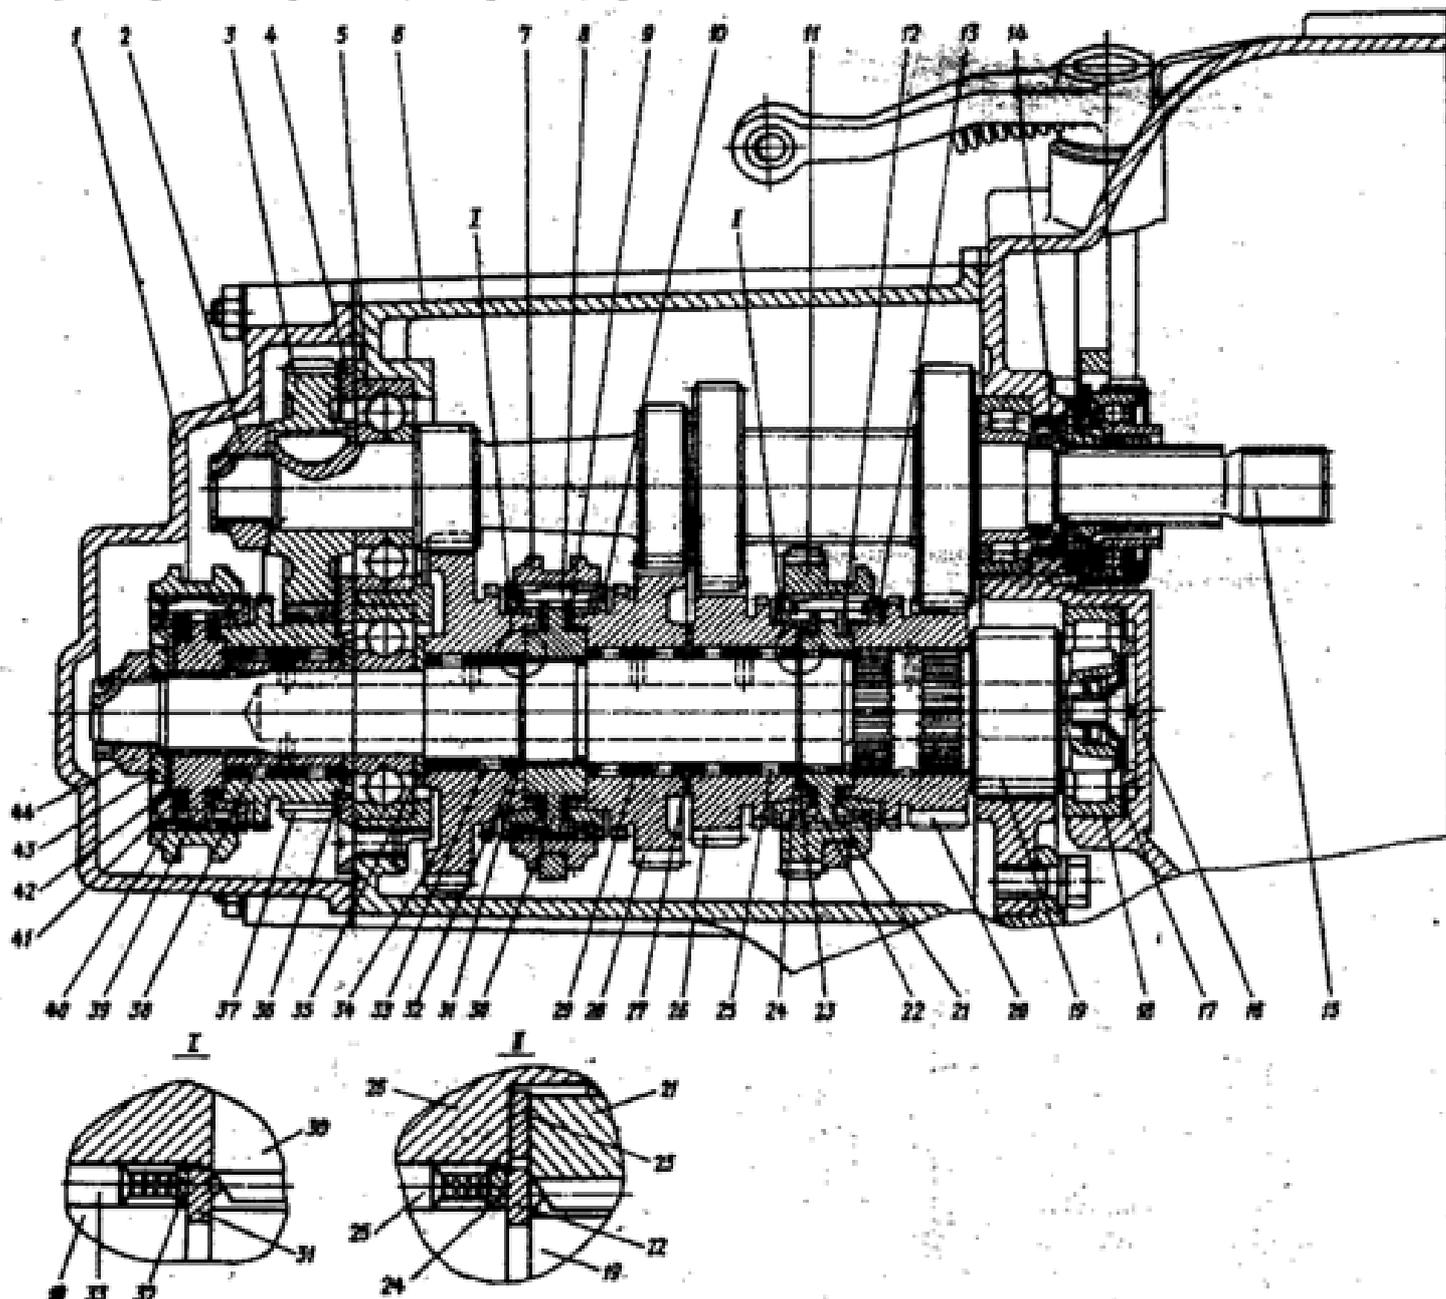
Коробка передач, продольный разрез: 1 - задняя крышка; 2, 44 - гайки; 3 - ведущая шестерня пятой передачи; 4 - крышка подшипников; 5, 18 - подшипники; 6 - картер коробки передач; 7 - муфта включения первой и второй передач; 8 - сухарь синхронизатора; 9, 12 - пружины синхронизаторов первой-второй и третьей-четвертой передач; 10, 13 - кольца блокирующие синхронизаторов первой-второй и третьей-четвертой передач; 11 - шестерня ведомая заднего хода; 14 - манжета; 15 - ведущий вал; 16 - картер сцепления; 17 - маслоотражательная шайба; 19 - шестерня-вал ведущая главной передачи; 20, 26, 28, 34, 37 - ведомые шестерни четвертой, третьей, второй, первой и пятой передач; 21 - ступица ведомой шестерни заднего хода; 22, 31 - стопорные кольца; 23, 27 - упорные шайбы; 24, 32 - кольца; 25, 33 - игольчатые подшипники; 27 - проставочные кольца; 30 - ступица муфты включения первой и второй передач; 35, 36 - упорные шайбы; 38 - распорная втулка; 39 - ступица муфты пятой передачи; 40 - муфта включения пятой передачи; 41, 42 - упорные шайбы сухарей пятой передачи; 43 - шайба упорная
